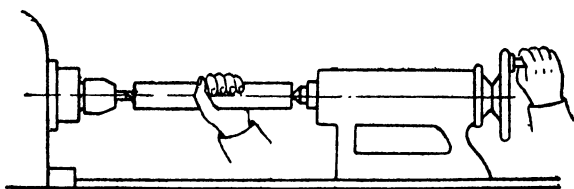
Зацентровка заготовки на токарно-винторезном станке.
